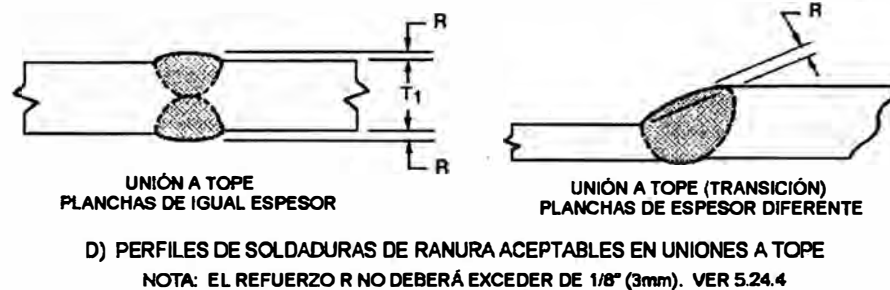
perfiles de soldadura aceptable e inaceptable
